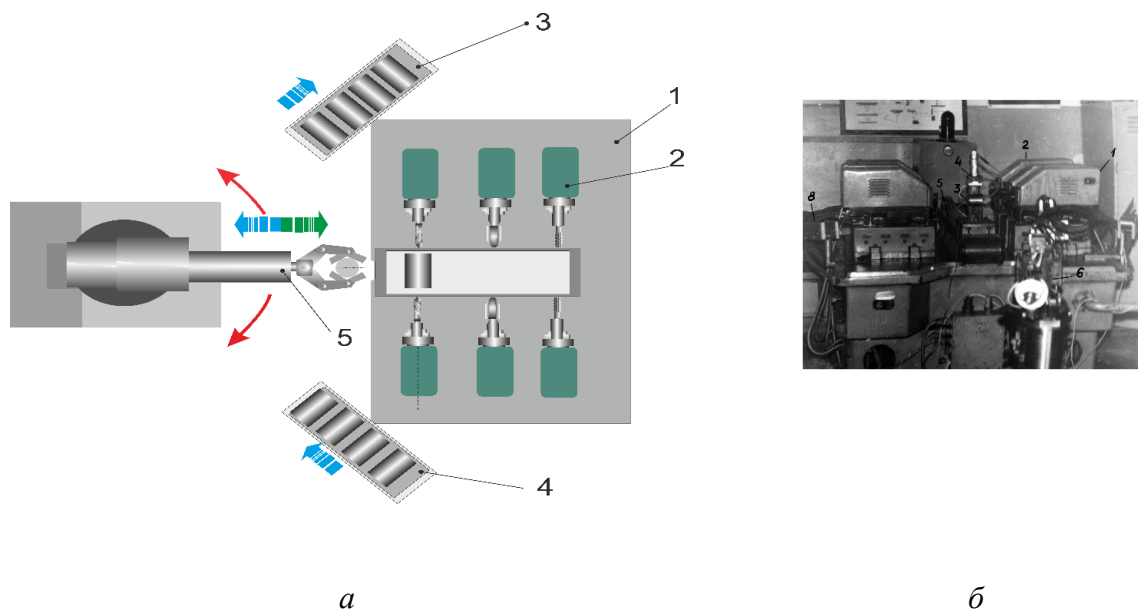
ГПМ для резбообработки отверстий на торцах цилиндрической детали (а): 1 – агрегатный станок А-26в (б); 2 – многошпиндельные переналаживаемые головки; 3, 4 – накопители; 5 – промышленный робот «Бриг-10Б»
